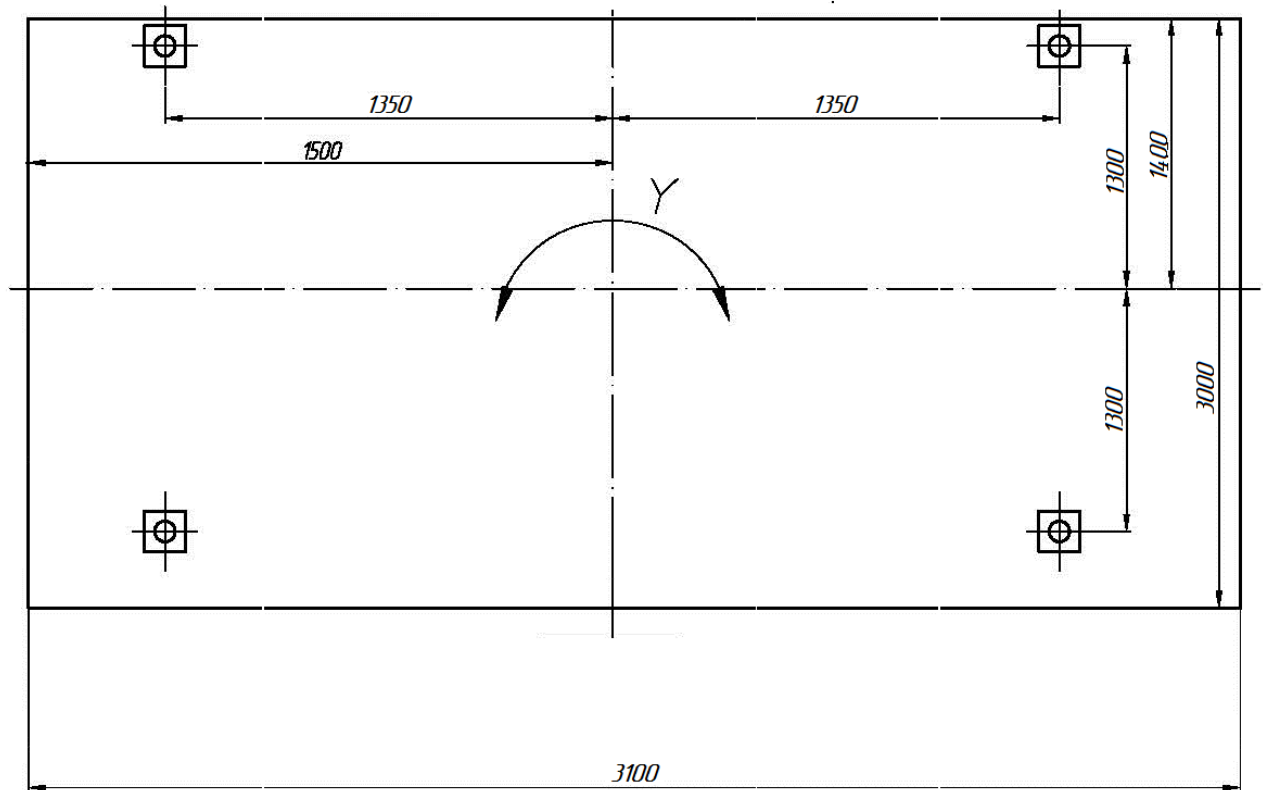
Схема кріплення кліті 730 до фундаменту
